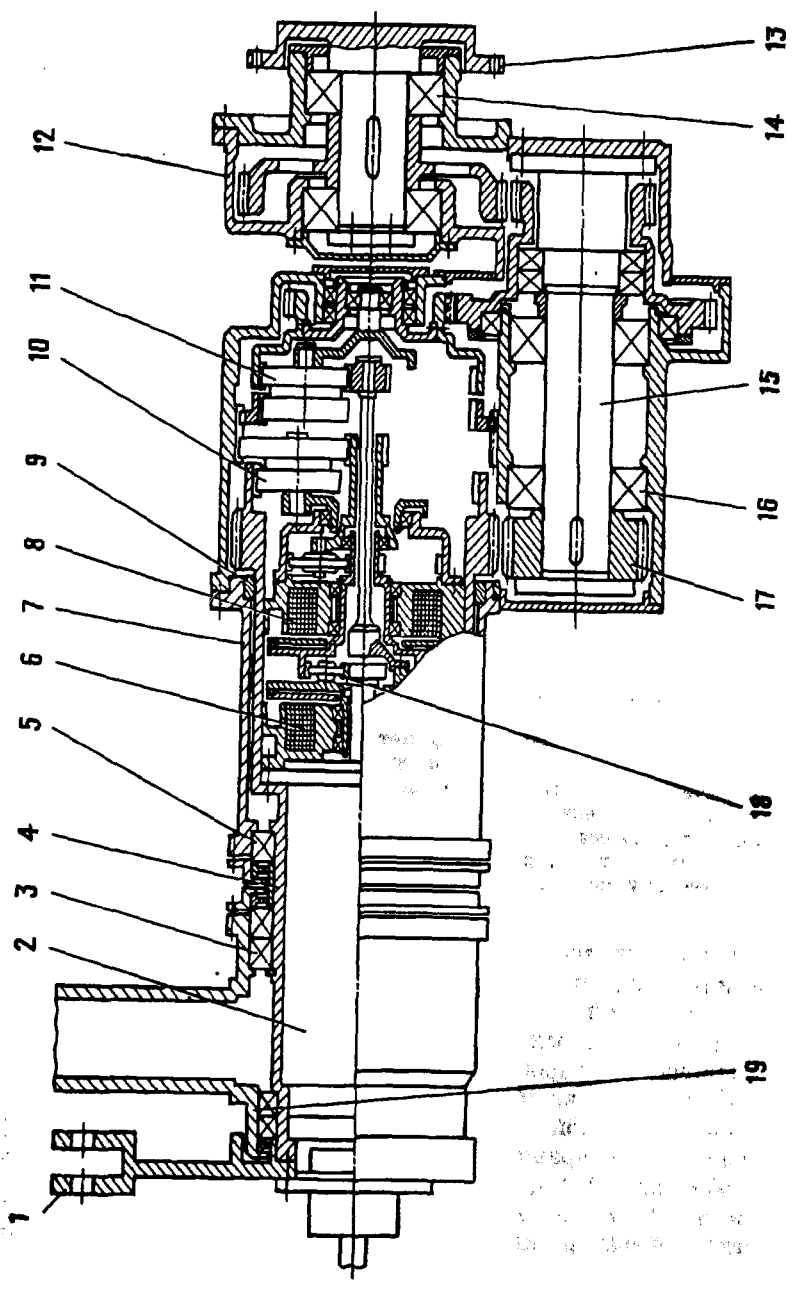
Колесно-шагающий движитель со встроенным приводом:
